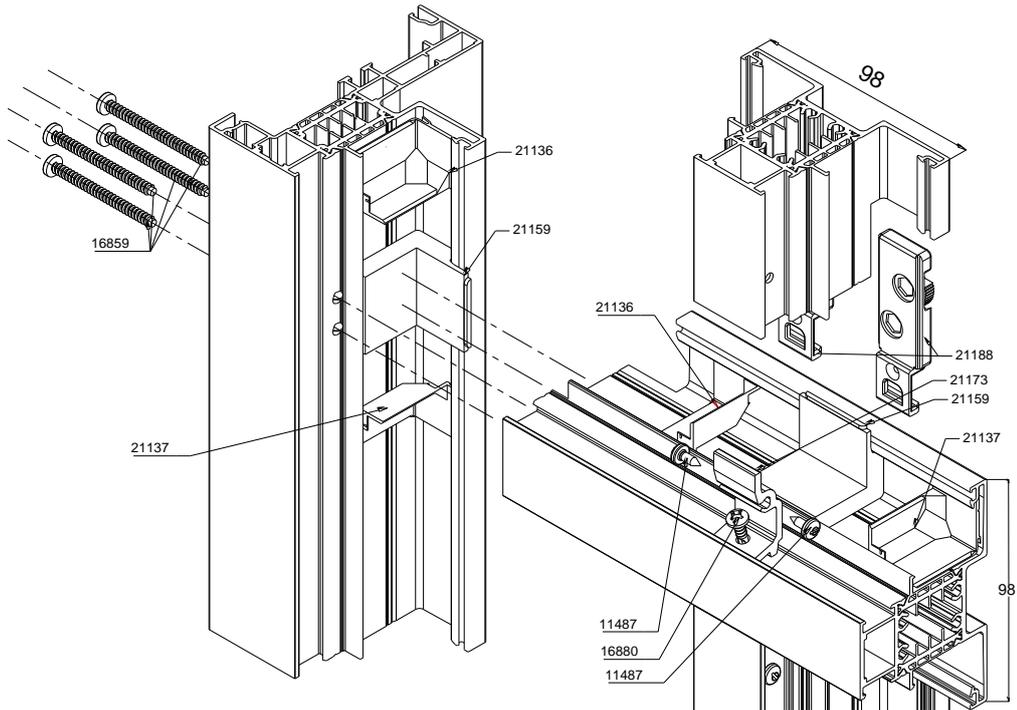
DETAILS D'ASSEMBLAGE MENEAU SUR SEUIL
